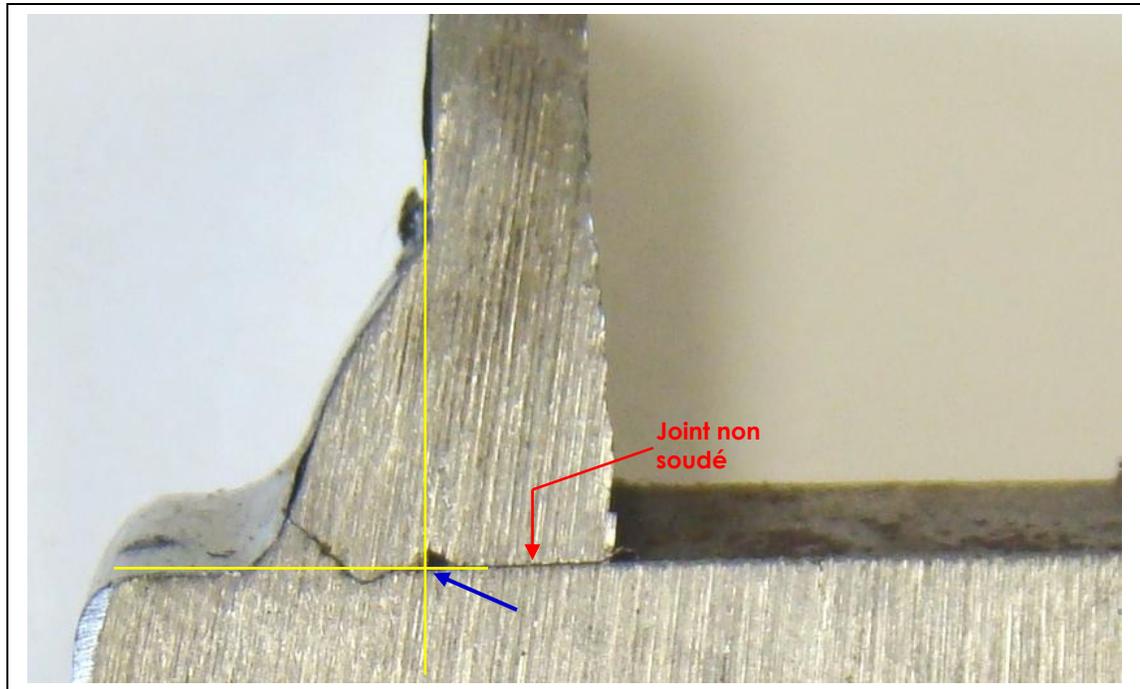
Fissure à la racine du cordon de soudure 2GE - surface int.
